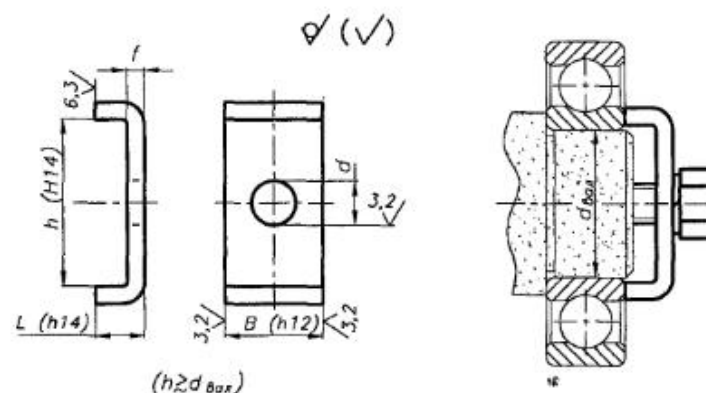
Конструкция и размеры стопорных скоб
